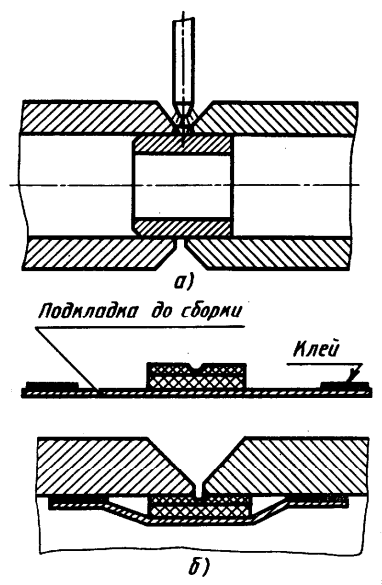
Сварка на съемных (удаляемых) подкладках
